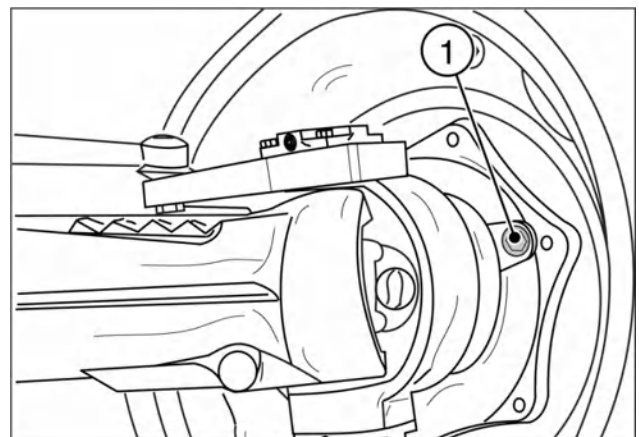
Передний колесный редуктор: пробка заливного отверстия (1).
